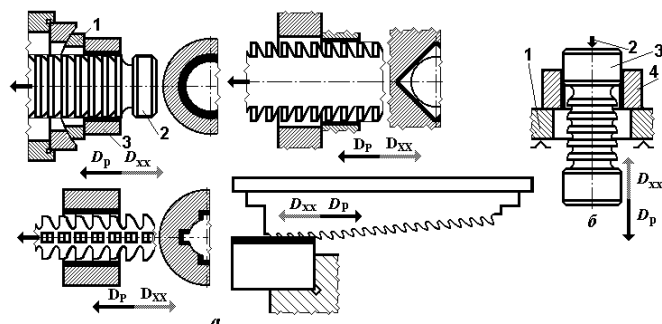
Основные технологические схемы протягивания: а – протягивание: 1 – плавающая опора; 2 – протяжка; 3 – заготовка; б – прошивание: 1 – стол; 2 – шток поршня; 3 – прошивка; 4 – заготовка; D_p – движение резания; D_{xx} – обратный ход.
